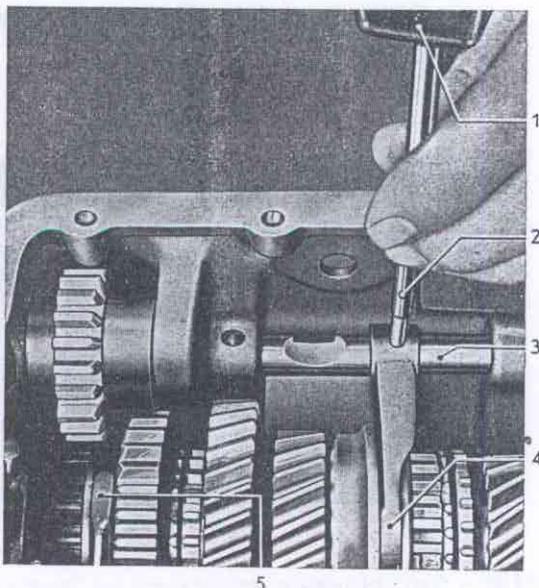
Spannstift aus Schaltgabel herausschlagen
